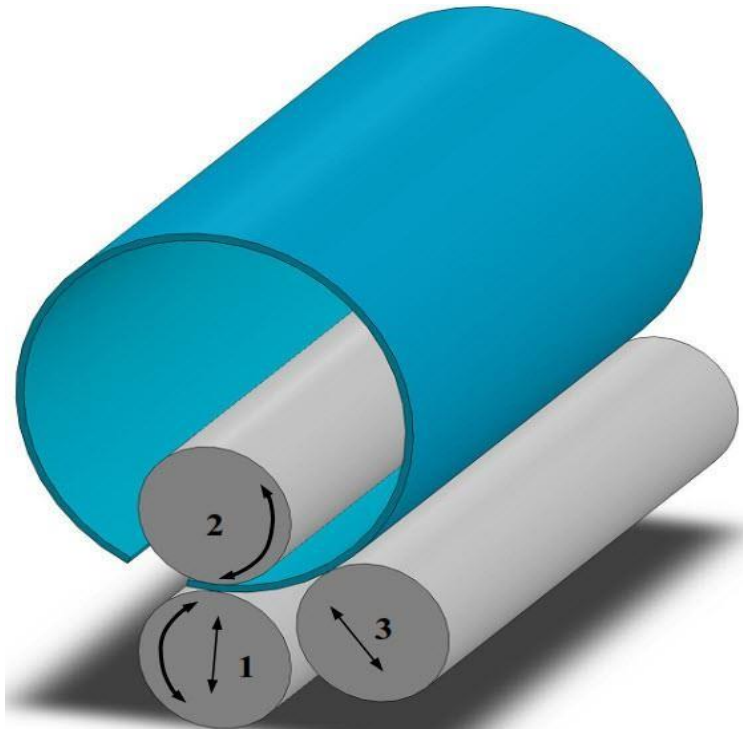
Configuración Asimétrica de Tres Rodillos. Fuente (Hoang Quan
